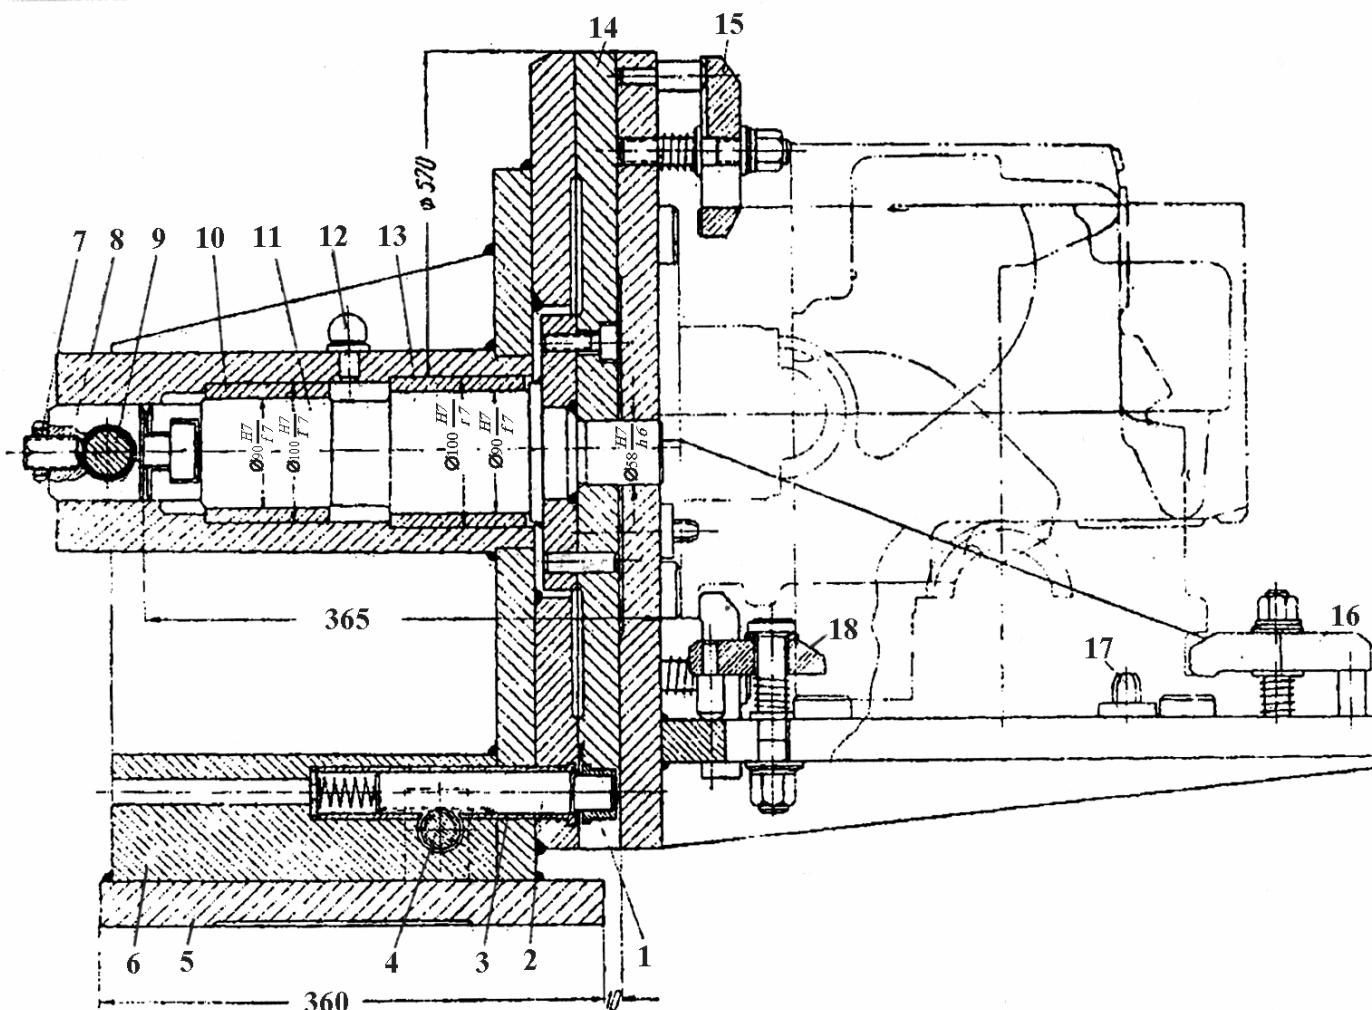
Поворотний стенд для кріплення блока циліндрів при ремонті:
